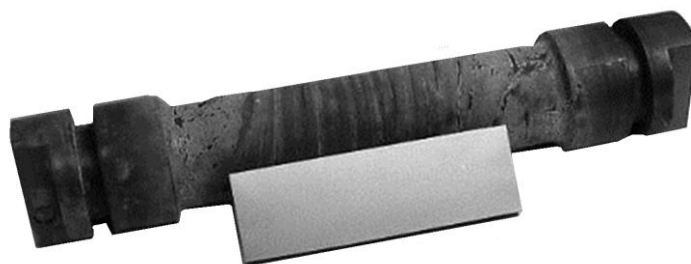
Внешний вид заготовки из сплава ВТ6 после 2-х компонентного нагружения.
